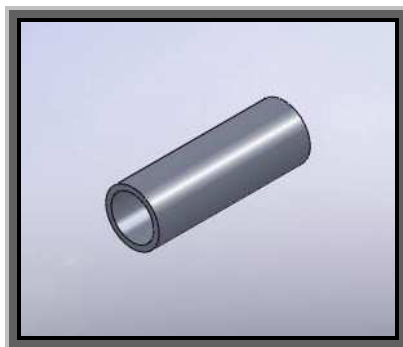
Vista isométrica de la parte inferior de la pieza de acople del conjunto.
